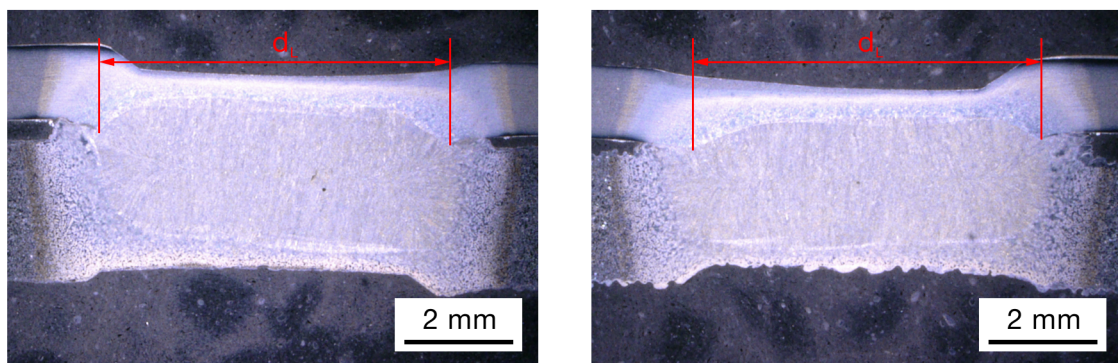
Punktschweißlinsen einer unbeschichteten Stahlgussprobe (links) und einer feuerverzinkten Probe mit durch Puls laser freigelegter Fügestelle (rechts)
